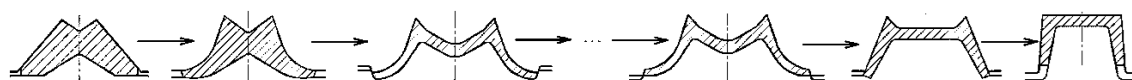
Схема развернутой швеллерной калибровки прокатных валков
